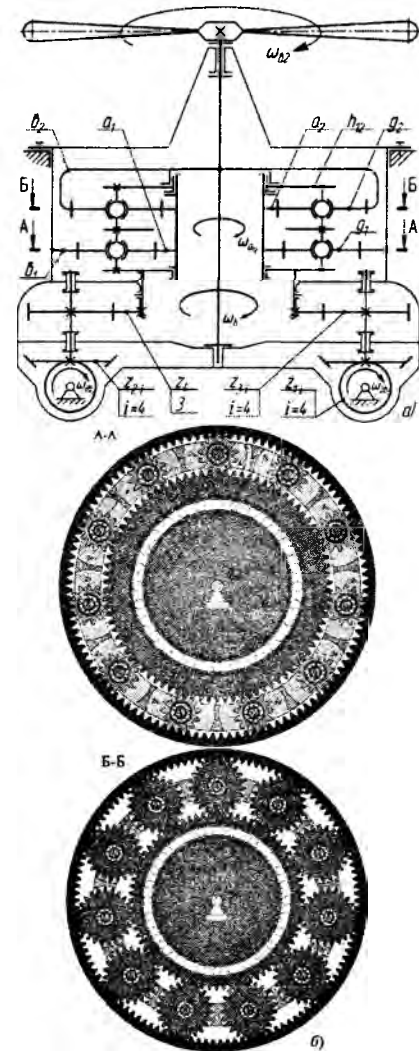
Рекомендуемый ТулГУ главный привод вертолета нового уровня: а) кинематическая схема, б) визуализация зубчатых зацеплений
